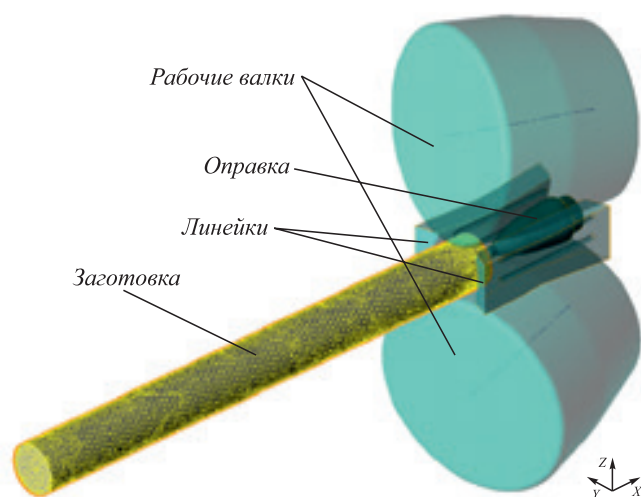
Трехмерная модель очага деформации для прошивки заготовки
